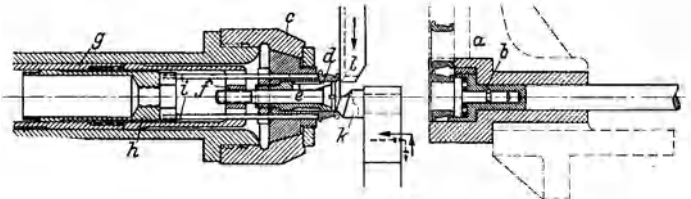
Bearbeitung der Stirnfläche und der Innenausrundung eines Innenringes für ein Kegelrollenlager.
